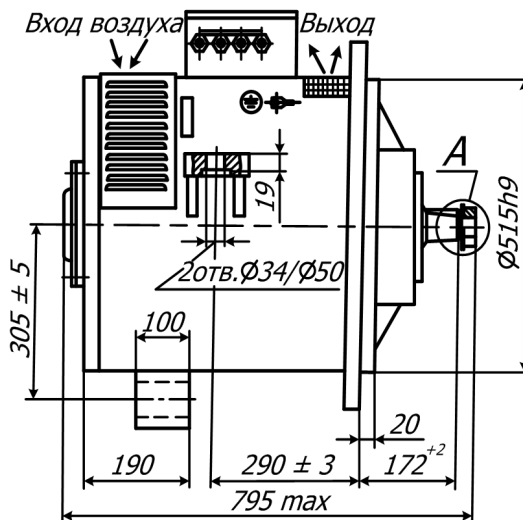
Общий вид тягового электрического двигателя ДТН-45
